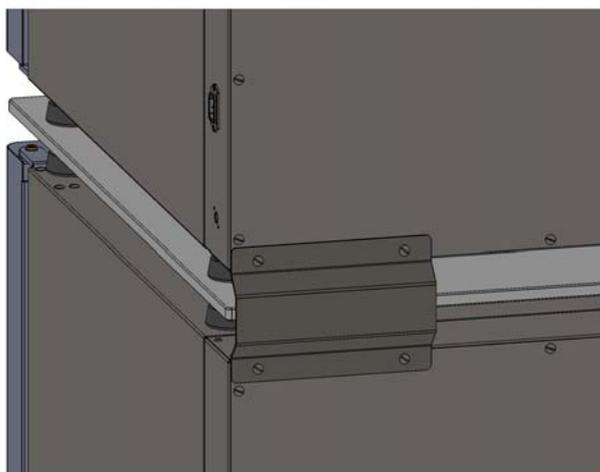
Fissaggio dell'adattatore a piastra all'apparecchio inferiore
